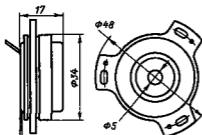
Габаритные и установочные размеры датчика угла ДУ-34-1
